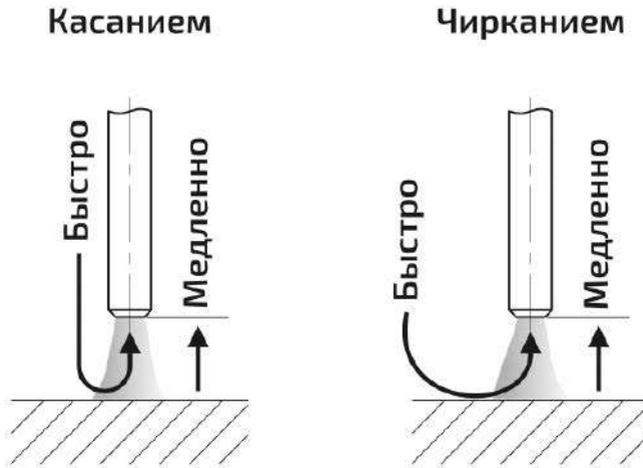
Способы зажигания сварочной дуги.
